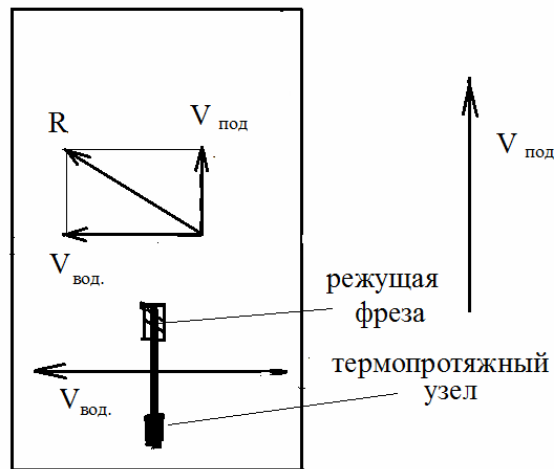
Кинематическая схема привода калибровально-шлифовального механизма с поступательно-колебательным движением
